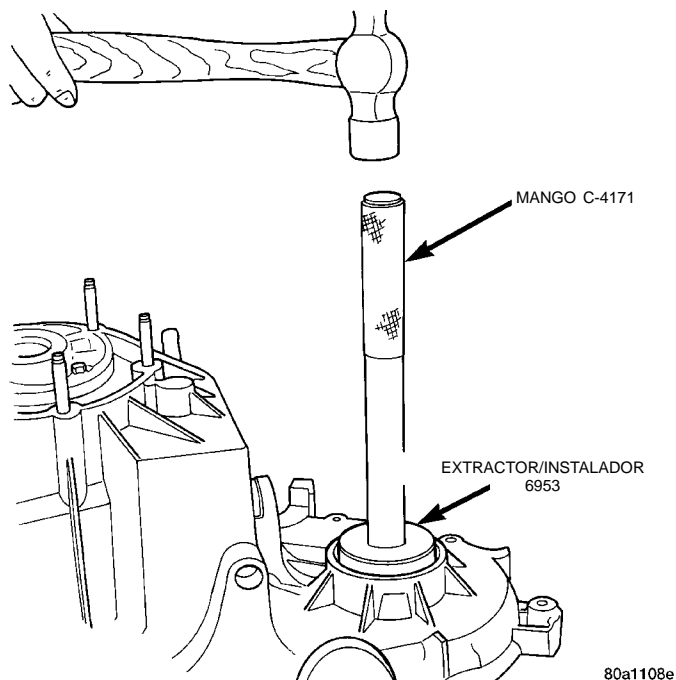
Desmontaje del cojinete delantero del eje transmisor
